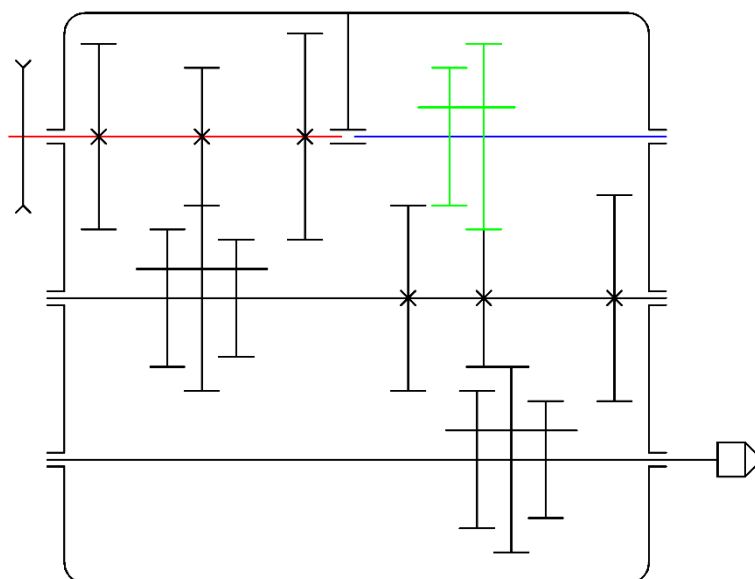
Prevodovka so šiestými ozubenými kolesami
